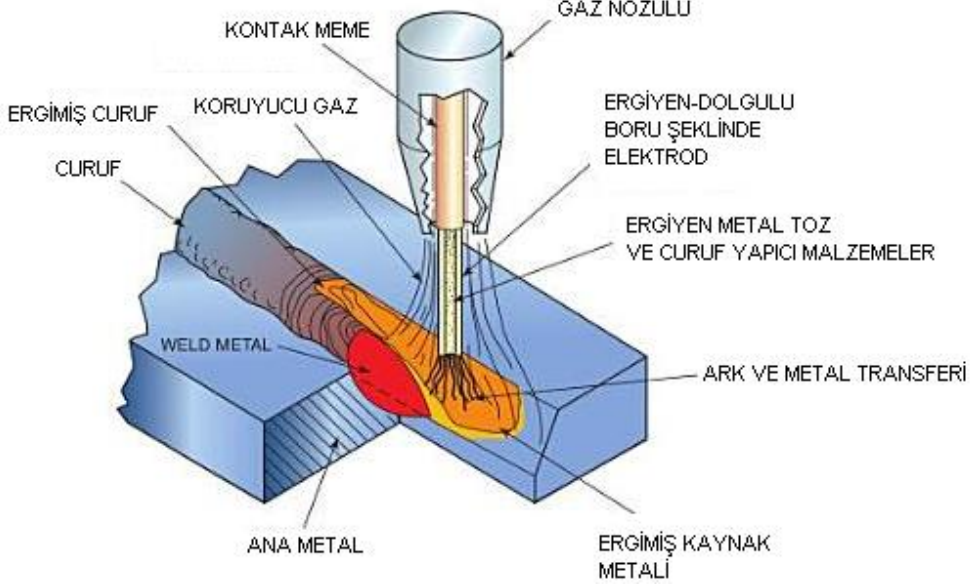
Paslanmaz çelik özlü teller ile yarı otomatik ve otomatik kaynak uygulamaları (Böhler Welding)
